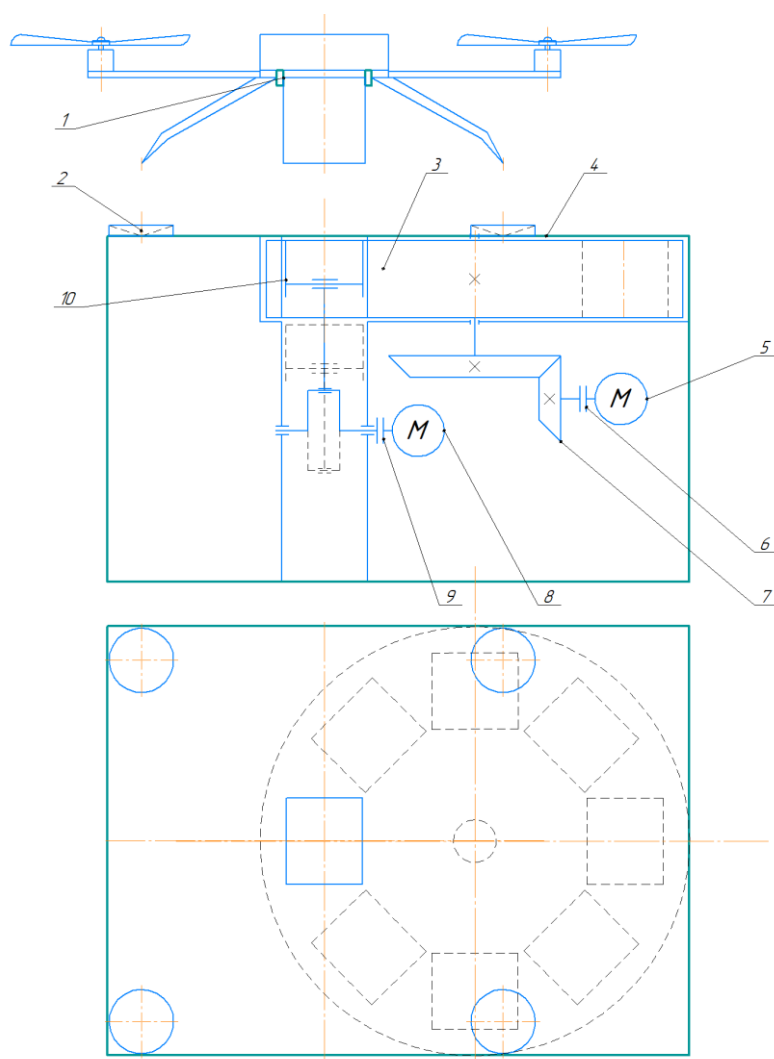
Станция для замены аккумуляторных батарей. 1 – защелки с электромагнитным приводом, 2 - конические ловители, 3 - барабан револьверного типа, 4 – корпус станции, 5 – шаговый двигатель, 6 – муфта, 7 – конический редуктор, 8 – сервопривод, 9 – муфта, 10 - кривошипно-шатунный механизм
